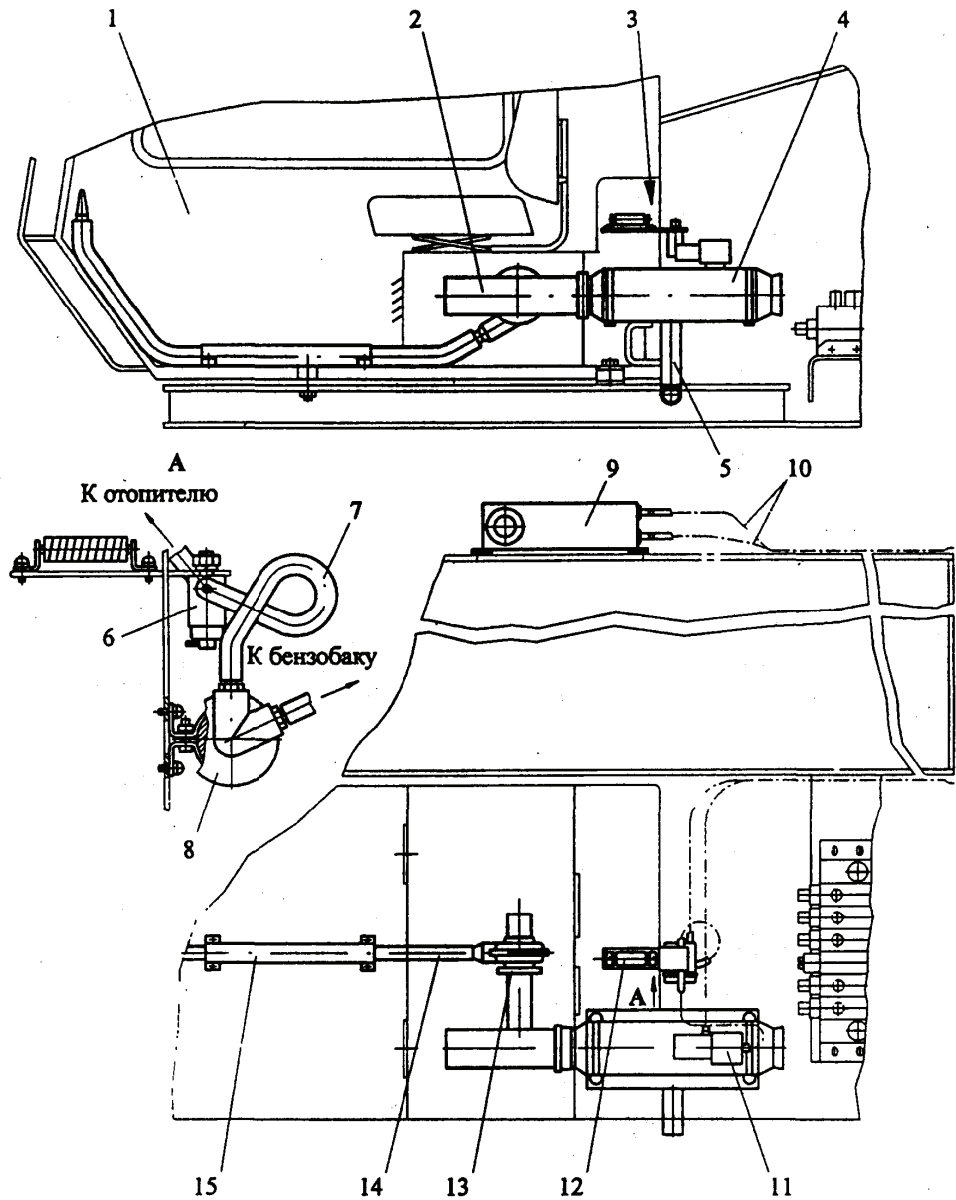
Система обогрева кабины грузоподъемного крана на специальном шасси автомобильного типа: 1 – кабина крановщика; 2 – воздуховод; 3 – ниша кабины; 4 – отопительная установка; 5 – труба; 6 – бензоотстойник; 7, 10 – бензопроводы; 8 – бензонасос; 9 – бензобак; 11 – регулятор подачи бензина; 12 – электросопротивление; 13 – вентилятор; 14 – шланг обогрева переднего стекла; 15 – щиток
